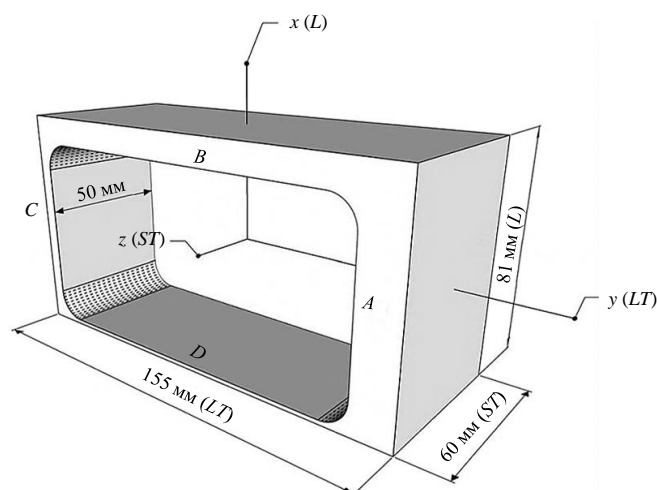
Геометрическая форма и размеры детали из сплава 7449 [24]
